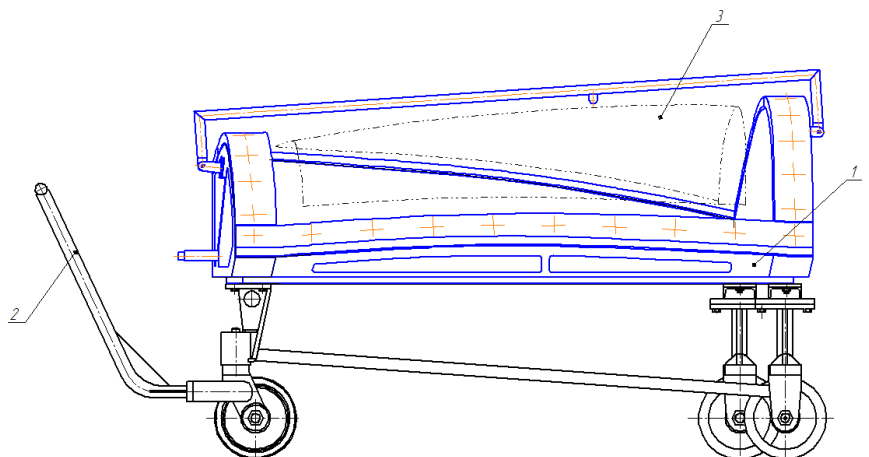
Приспособление для пневмоформования лобового стекла изд.«226».
